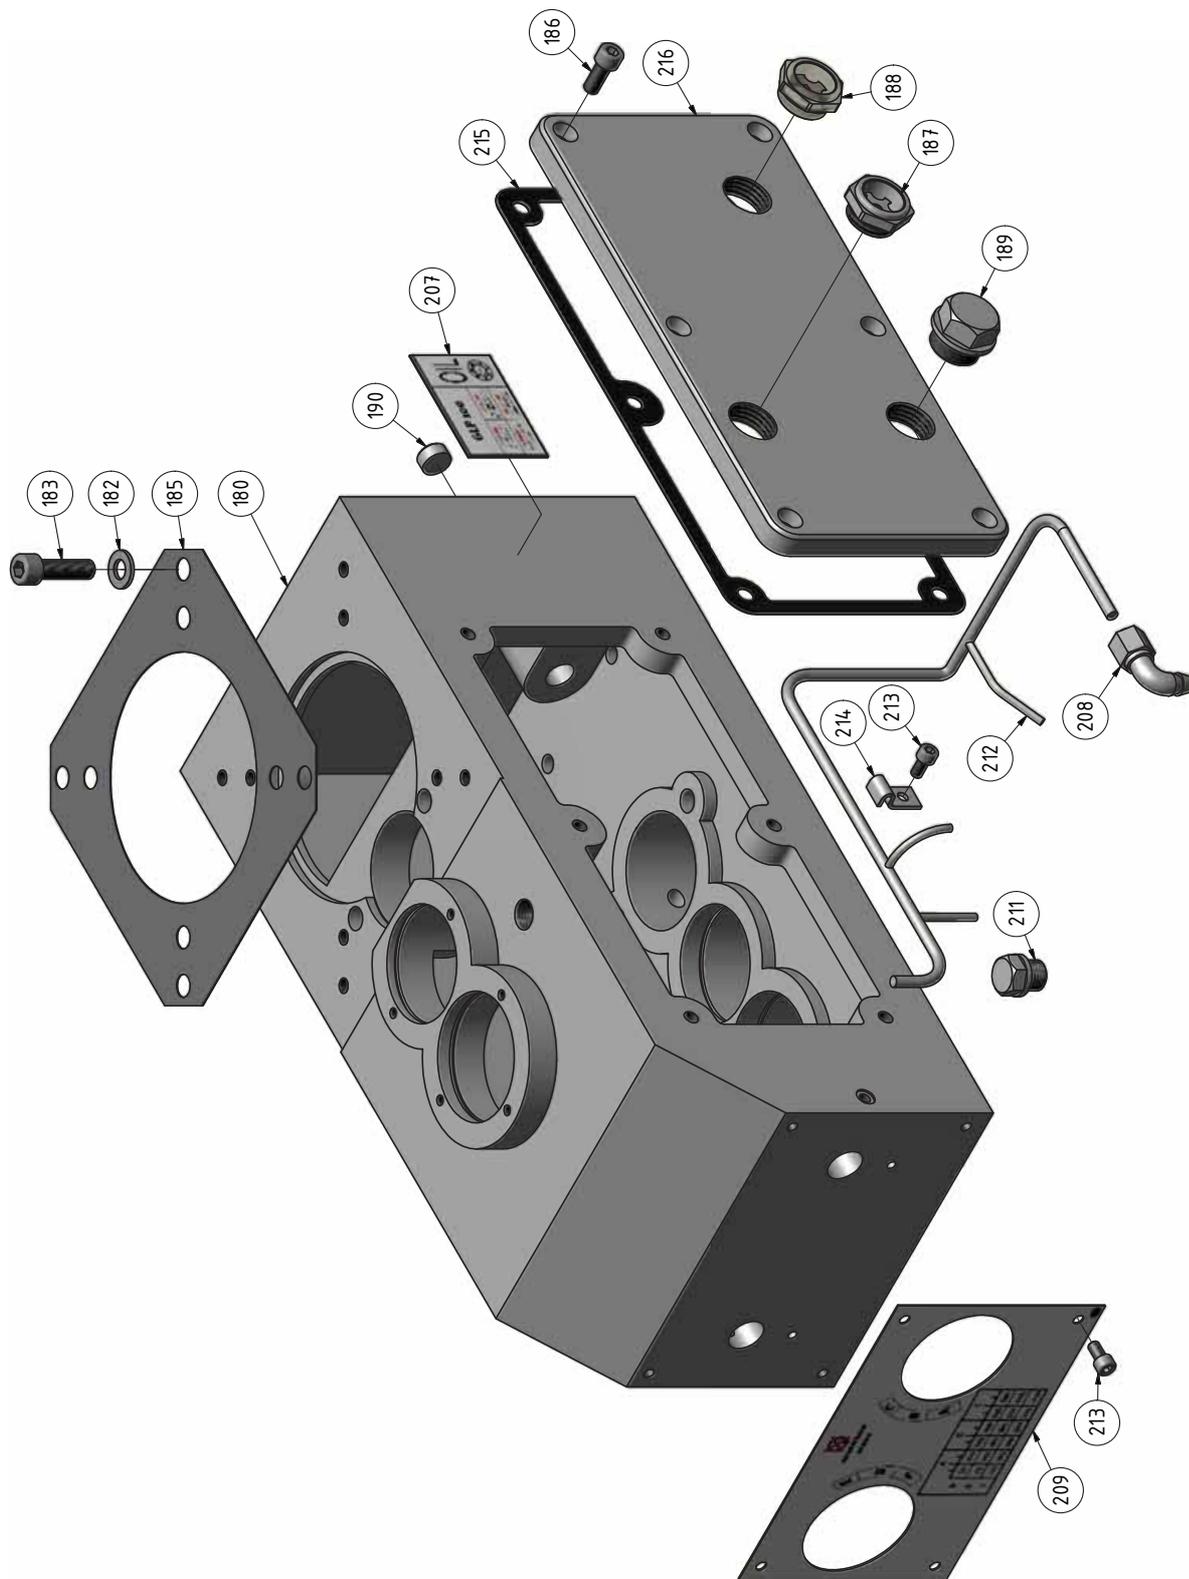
Getriebe Bohrspindel 4 von 4 - Gear box main spindle 4 von 4
